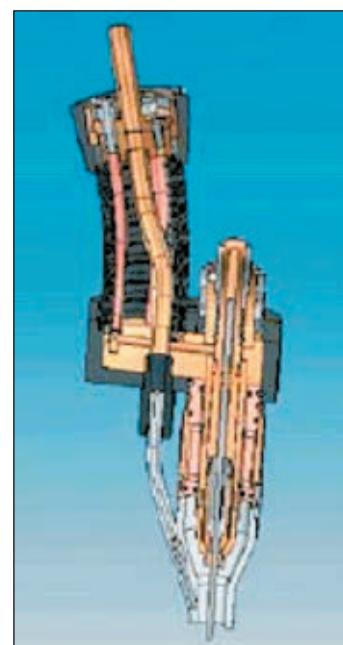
Обычная TIG-горелка с боковой подачей проволоки
